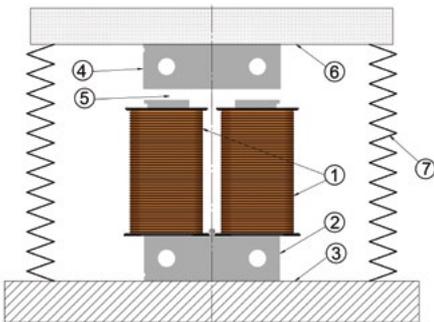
Schwingmagnet OAC... eingebaut im Schwingssystem
